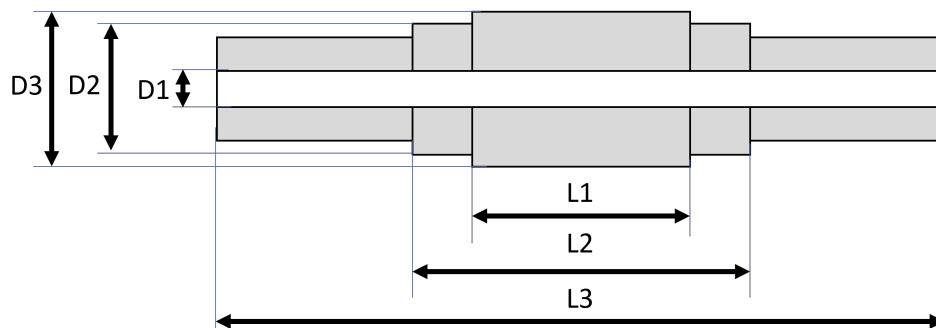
Dimensions de l'arbre pour le calcul des résistances
